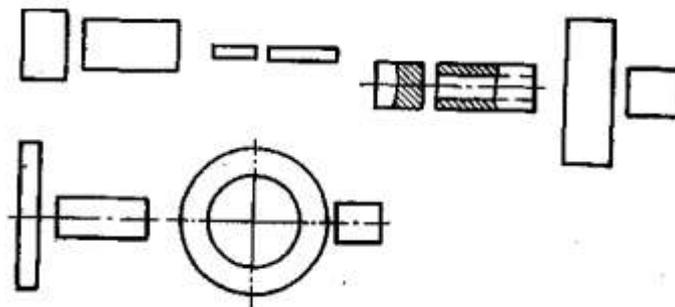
Типы сварных соединений стыковой сварки.
